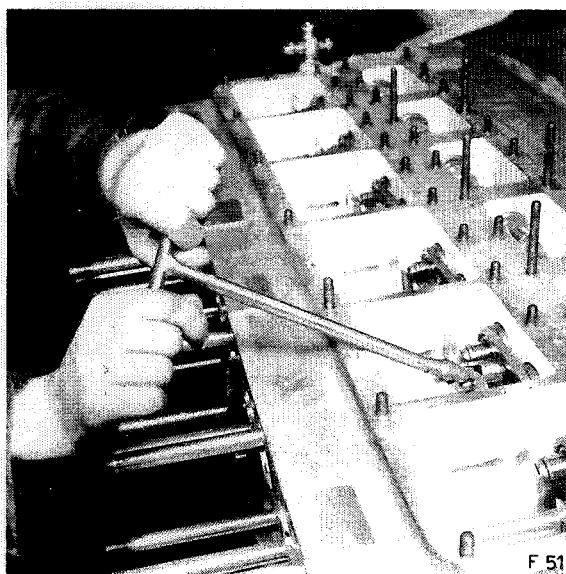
Lösen der Befestigungsmuttern für das Schwungradgehäuse
